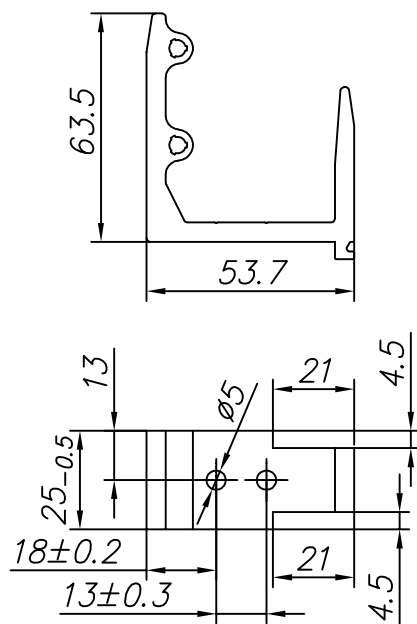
Изготовление соединителя FLGU.400.0913
